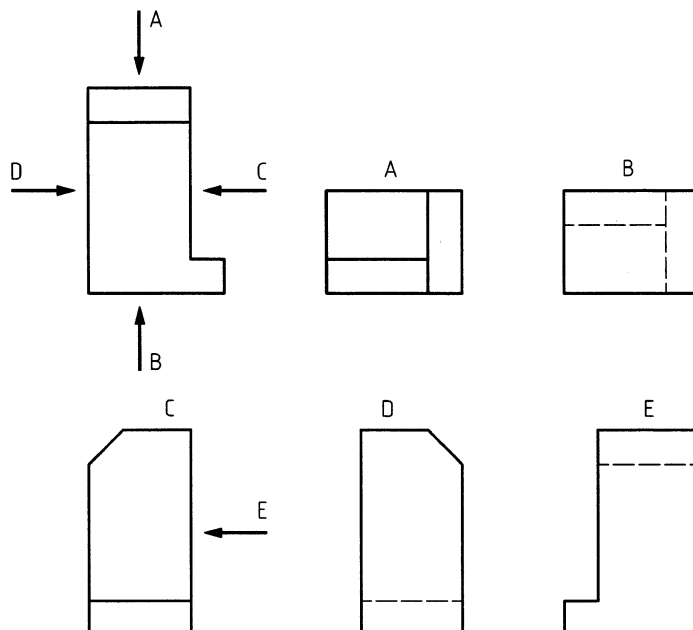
Kennzeichnung der zugehörigen Ansichten
